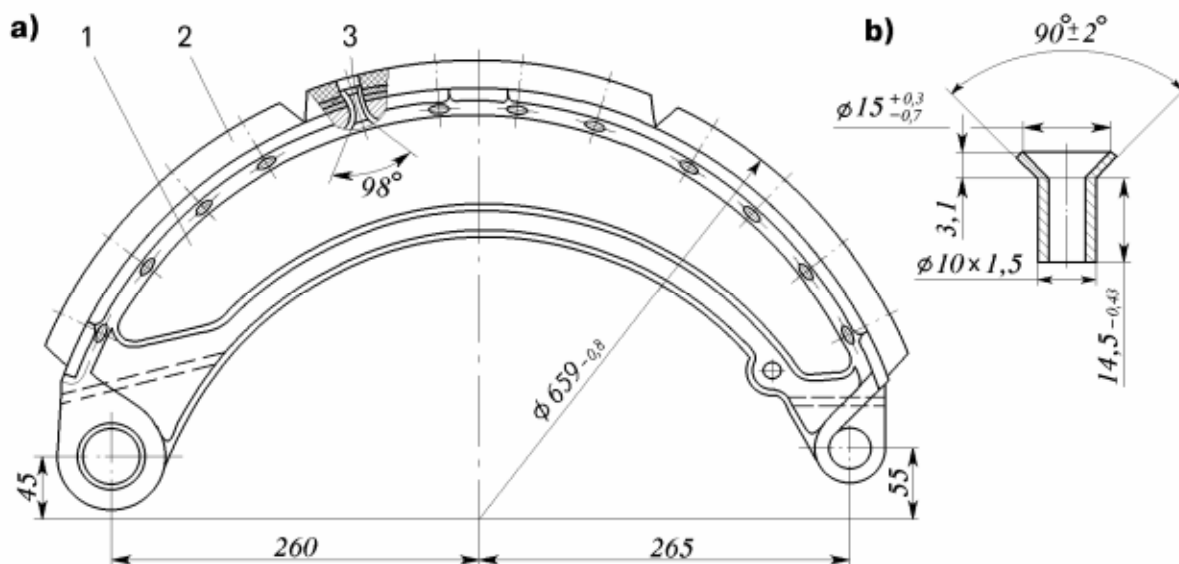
Колодка тормозного механизма рабочей тормозной системы (эскизы для обработки):
